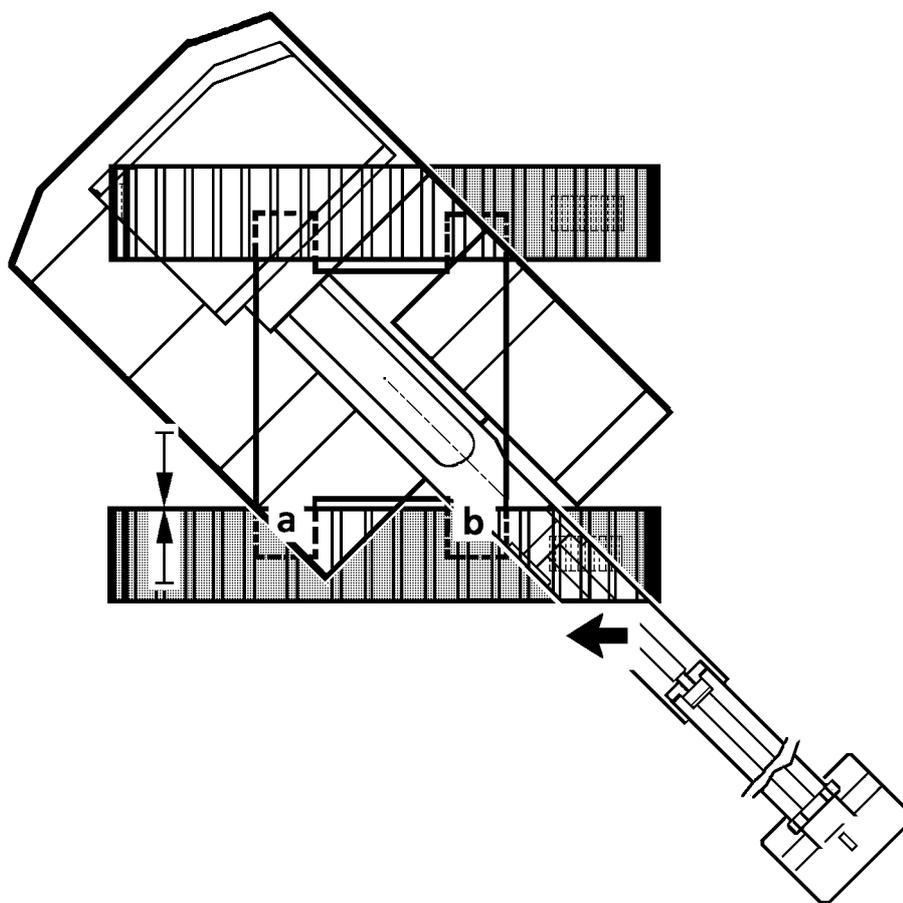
Retracción de la viga longitudinal del lado de la rueda guía (delante)
